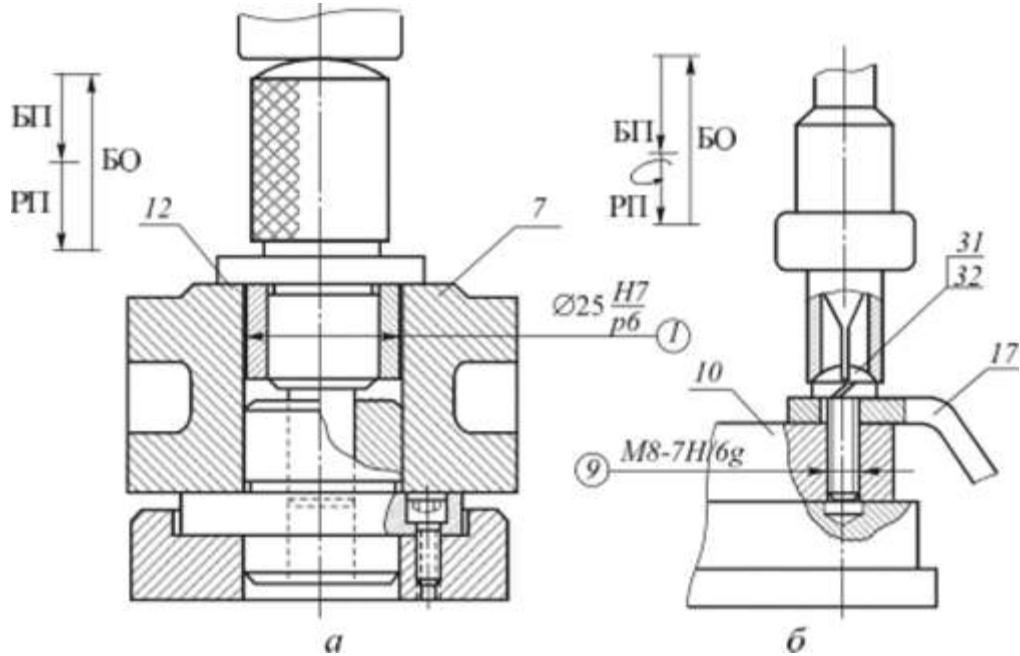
Примеры технологических эскизов сборки: а - запрессовки втулки 12 в корпус 7.6 - свинчивания детали 12 с корпусом 10
